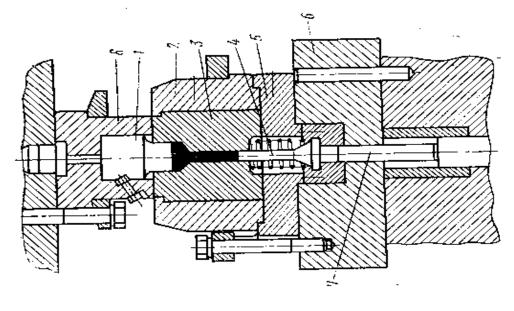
Схема штампа для высокоскоростного выдавливания пазовой фрезы: 1 –пуансон; 2 – обойма матрицы; 3 – матрица; 4 – выталкиватель; 5 – переходная плита; 6 – опорная плита; 7 – выталкивающий стержень; 8 – блок пуансонов
